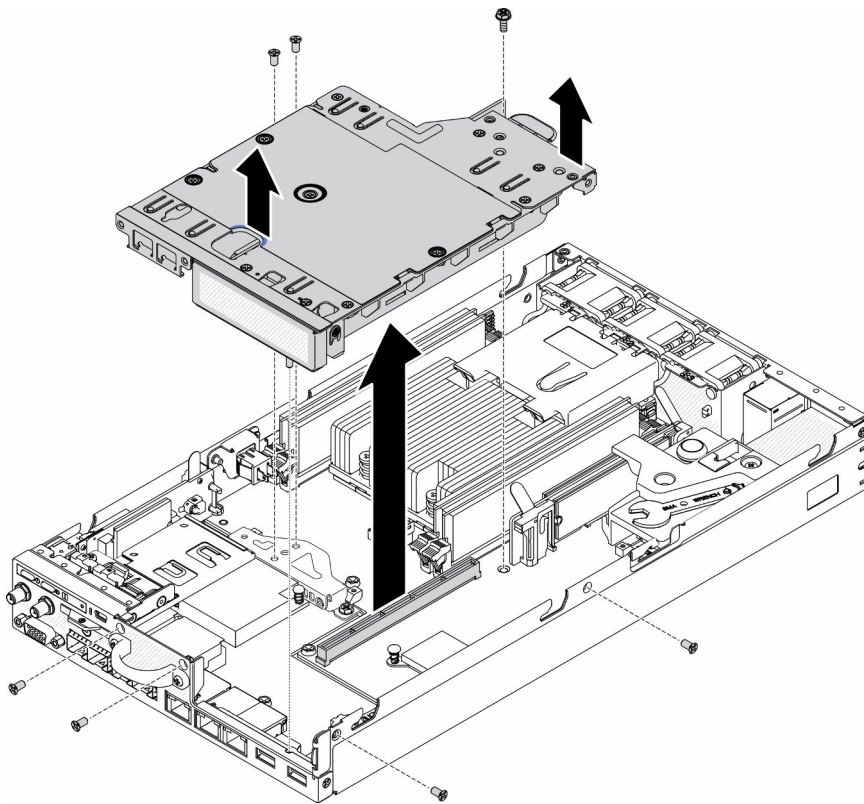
PCIe-Adapterkartenbaugruppe entfernen
